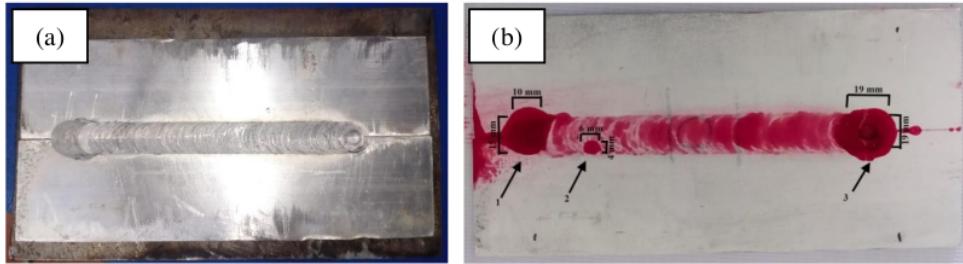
Spesimen 2 : (a) sebelum *test penetrant* dan (b) sesudah *test penetrant
